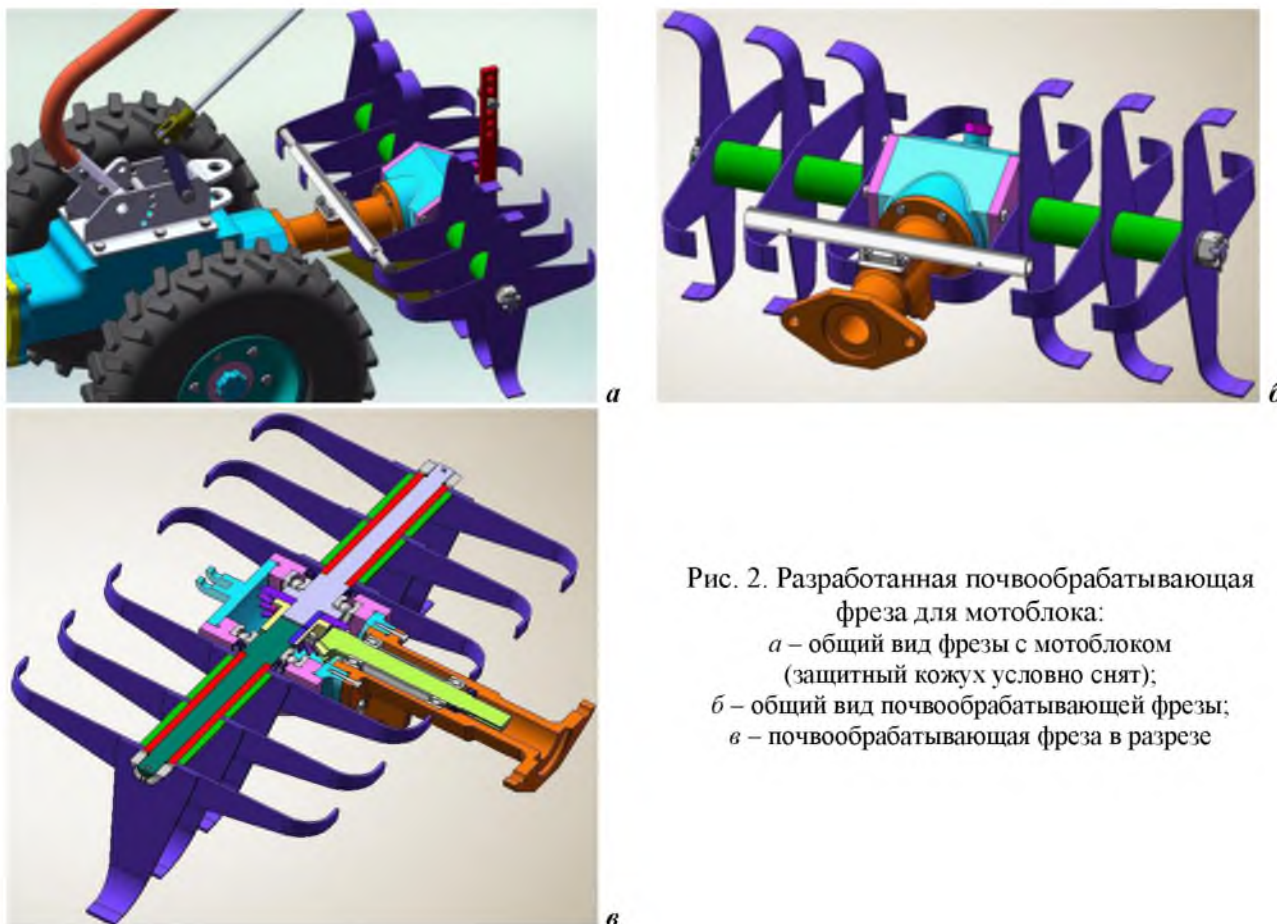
Разработанная почвообрабатывающая фреза для мотоблока:
